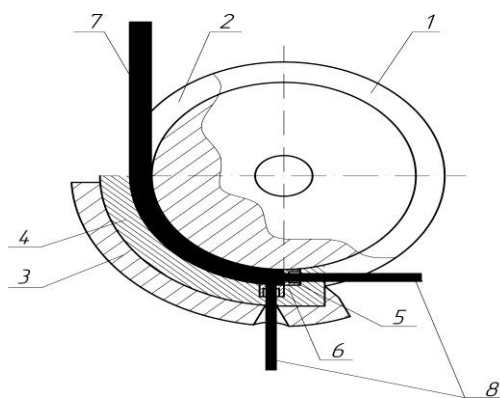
Схема непрерывного прессования способом Конформ:
